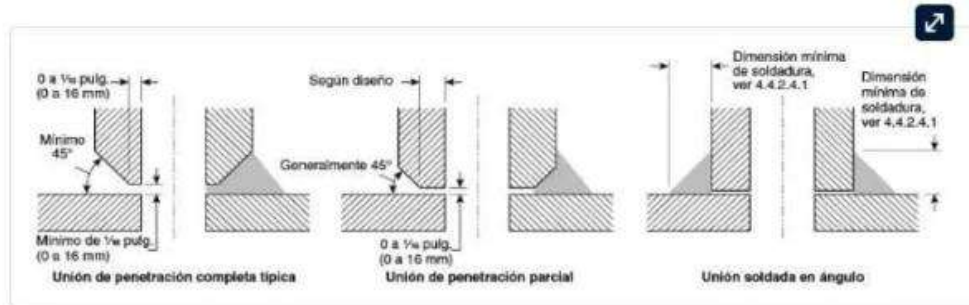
Descripciones de soldaduras. [13:Figura A.7.5.2.4.1]
